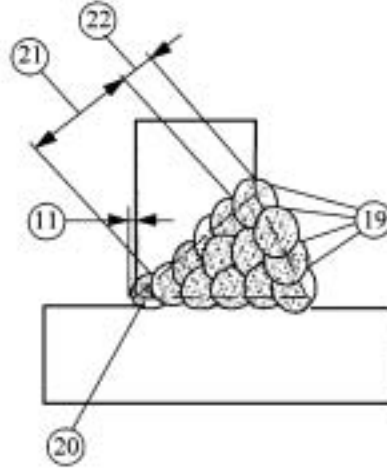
Köşe kaynak dikişleri için dikiş kalınlıkları
